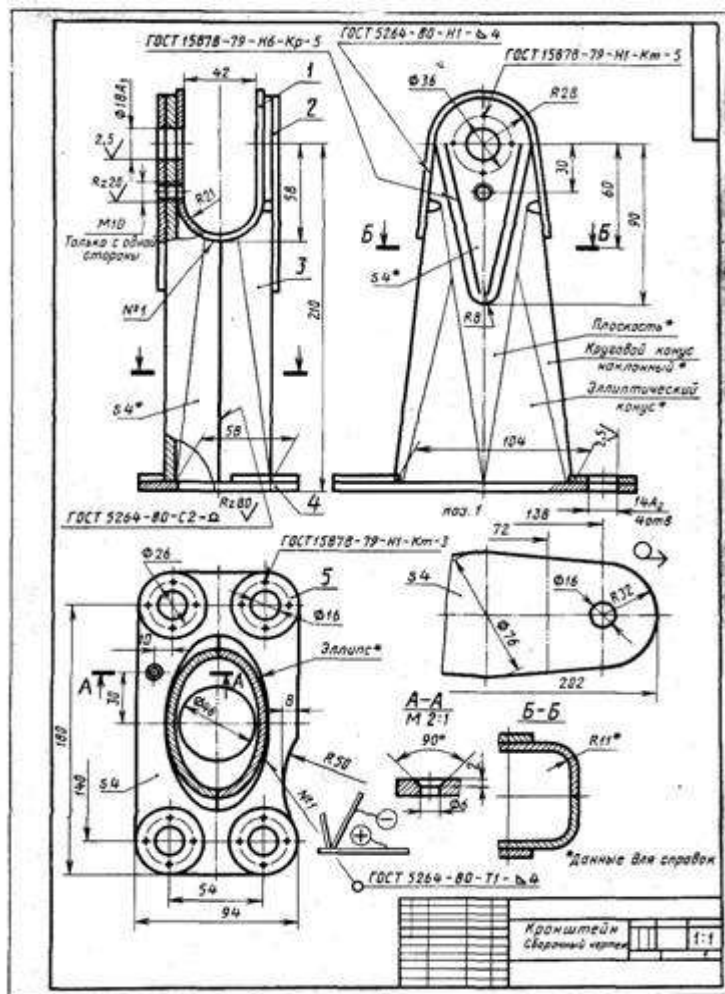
Чертеж сборочной единицы с различными типами сварных швов и видами сварки
